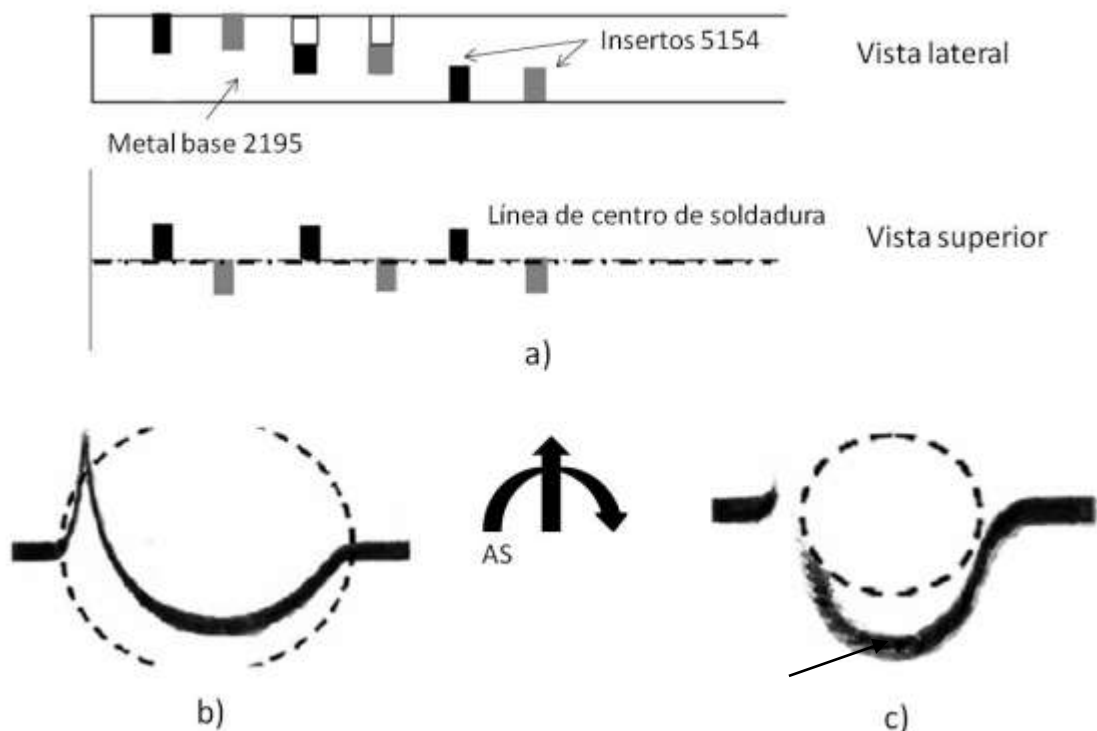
a) Localización de los marcadores embebidos, b) vista superior del patrón de flujo a 0.25mm de la parte superior de la soldadura (el círculo punteado hace referencia al hombro de la herramienta); c) Patrón de flujo a la mitad del espesor (el círculo punteado hace referencia al pin, la flecha señala el límite entre el MM de AS y RS). ⁽¹²⁾
